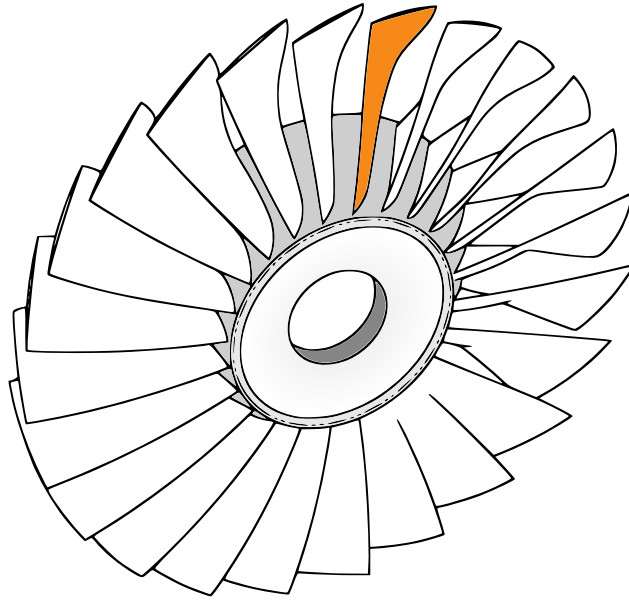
Roue aubagée, dont chaque aube (■) est liée mécaniquement au disque (□). Adapté de [2].
